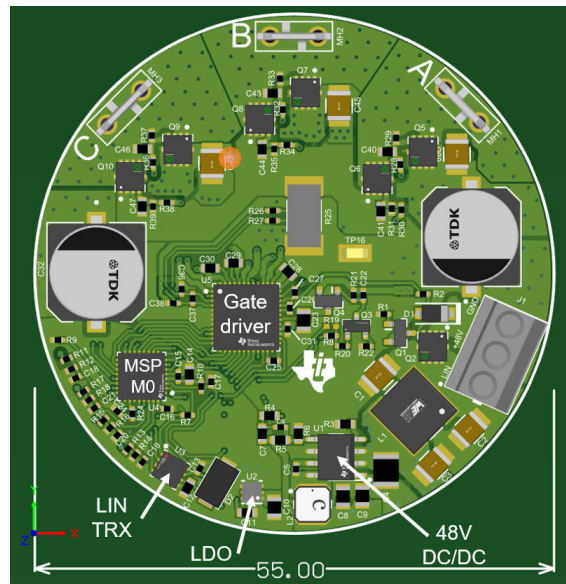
泵和鼓风机用紧凑型智能执行器 PCB
